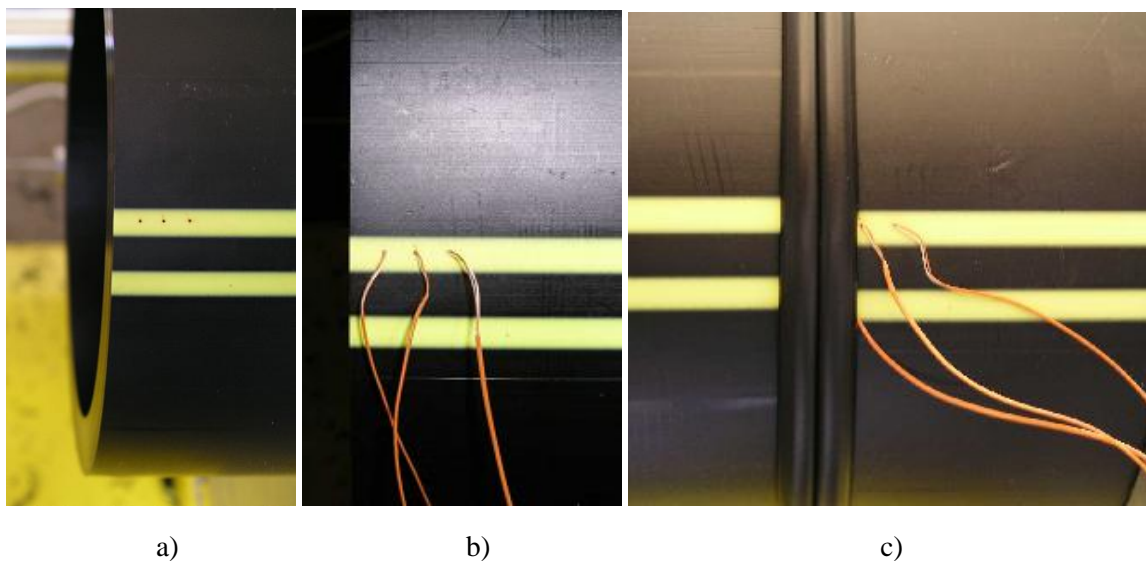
Positionnement des thermocouples dans les tubes : a) perçage des trous, b) mise en place des thermocouples, c) position des thermocouples après soudage
